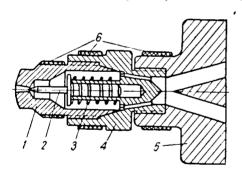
Сопло с запорной нглой: 1—сопло; 2—запорная игла; 3—пружина; 4—втулка; 5— нижекционный диялиндр; 6—электрообогрев.
